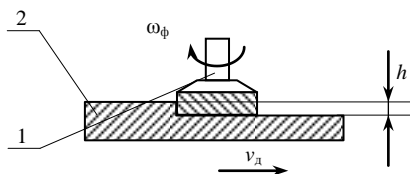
Принцип обработки металла на фрезерных станках:
